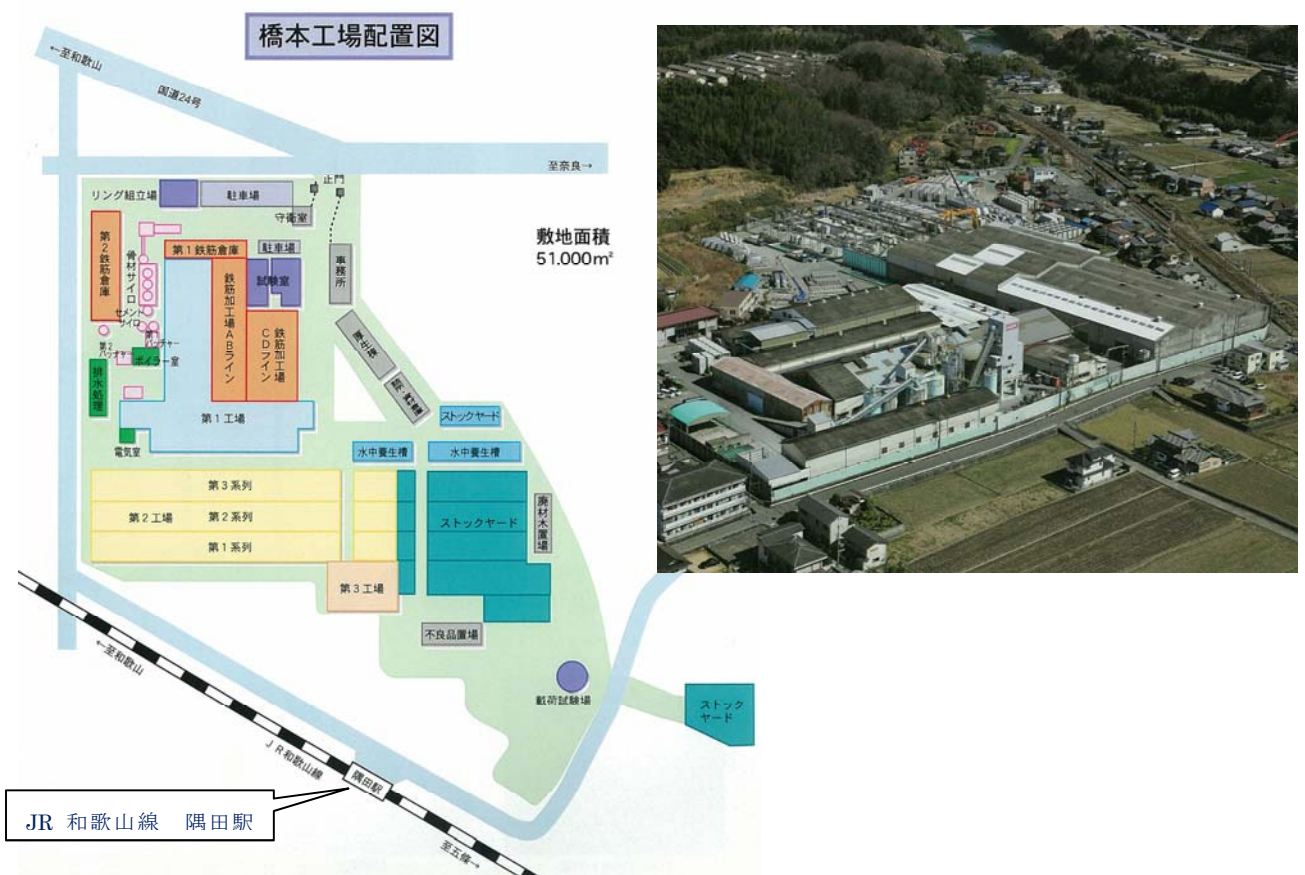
セグメント工場配置図・航空写真¹⁾
